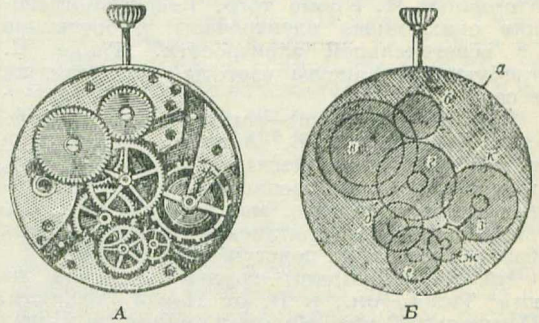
Карманные часы: А—внешний вид (задний); Б—схема механизма: а—корпус, б—колесо завода, в—пружинная коробка, г—минутное колесо, д—передаточное колесо, е—секундное колесо, ж—анкерное колесо, з—анкер, к—баланс.
